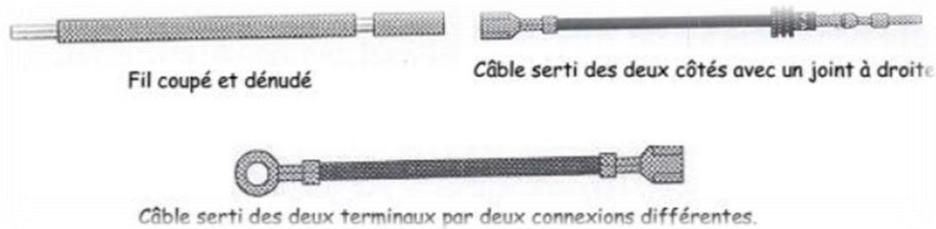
COUPAGE DENUDAGE SERTISSAGE DE CABLE.
